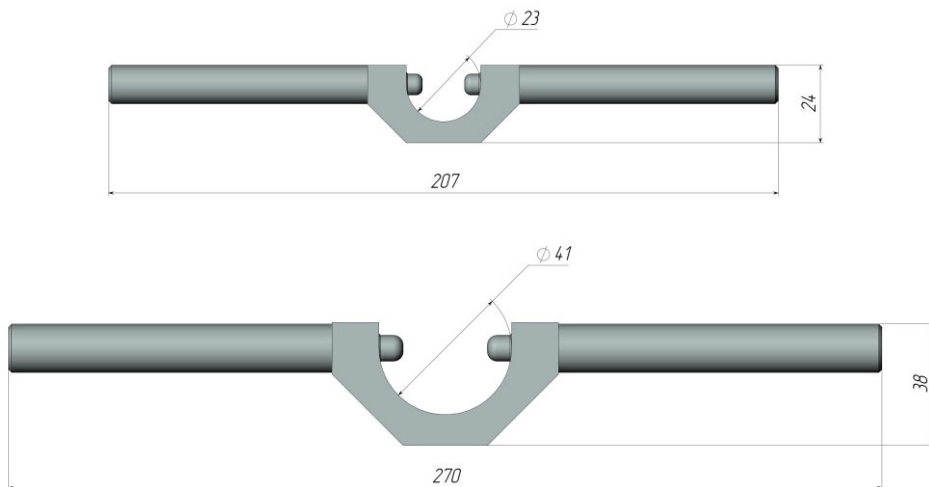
Приспособления для сборки (демонтажа)
